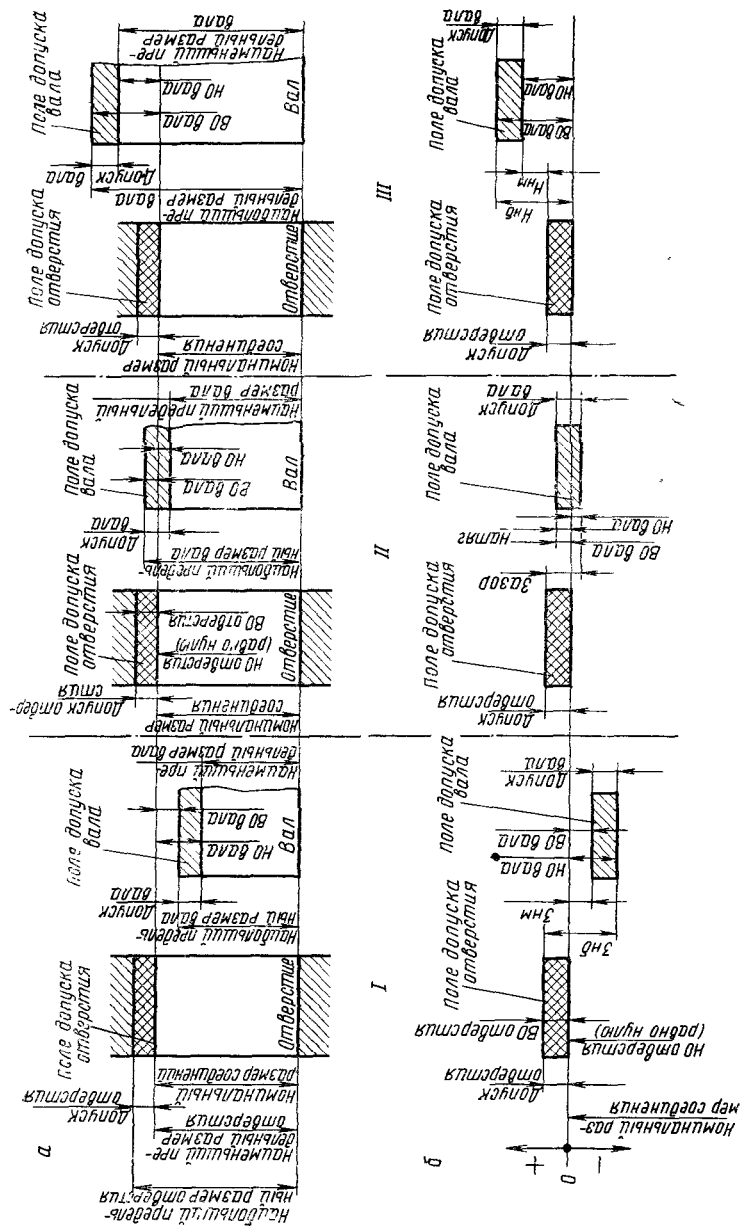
Схемы расположения полей допусков отверстия и вала при разных посадках:
